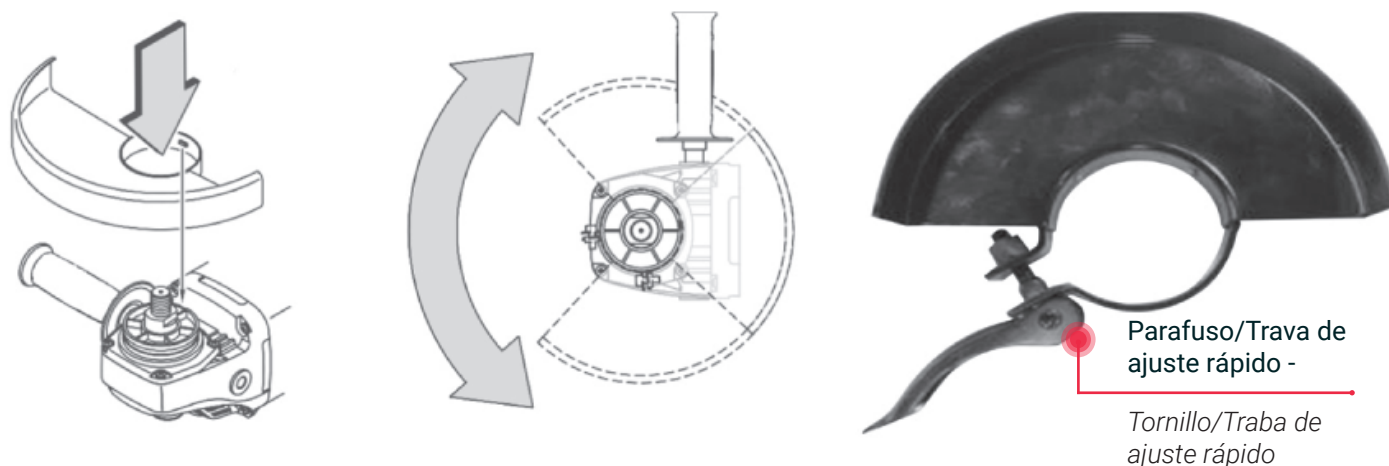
Montagem e posicionamento da capa de proteção / Montaje y posicionamiento de la cubierta de protección
